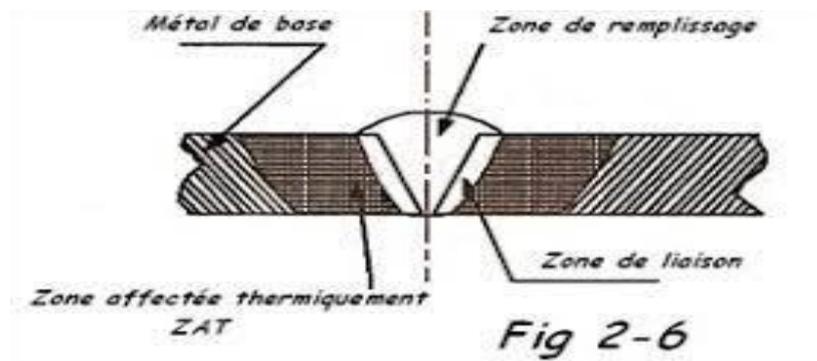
6: Différentes zones d'un assemblage soudé. [21]
